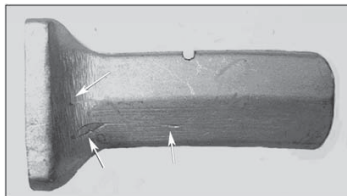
Дефекти у вигляді задривів і рисок на поверхні видавленої заготовки
